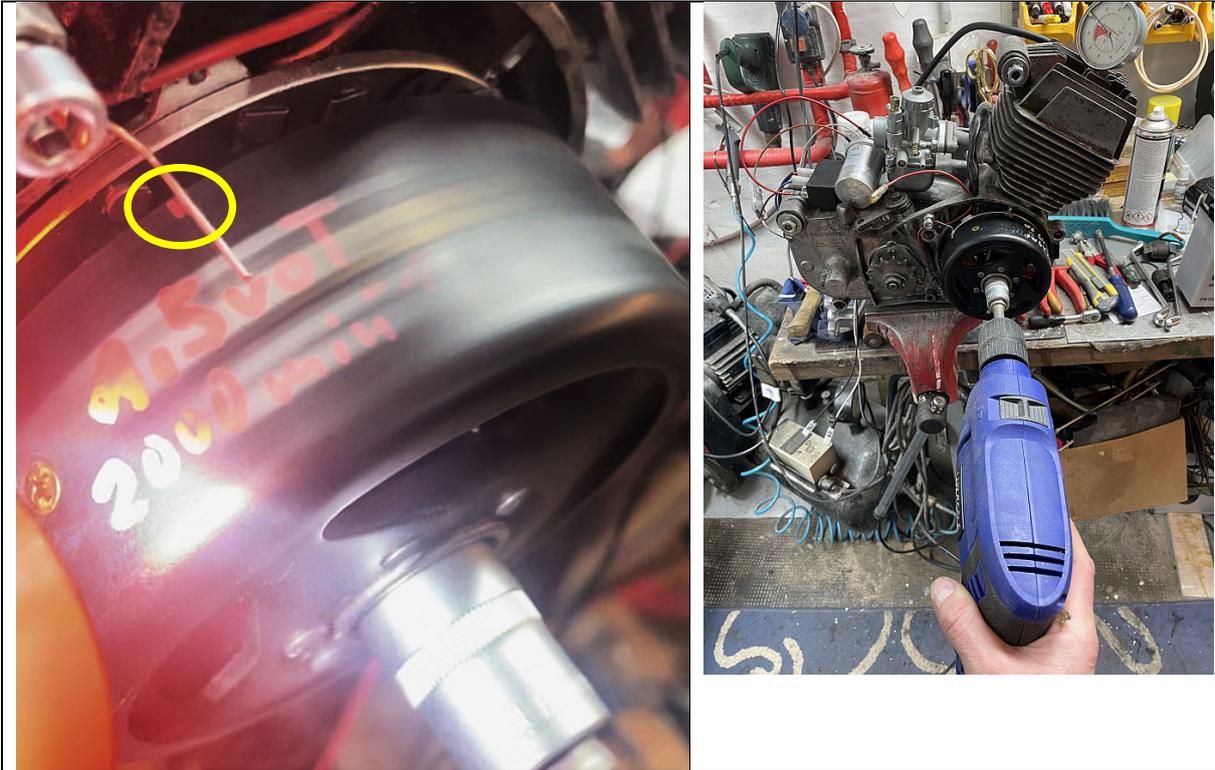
Zu früher Zündzeitpunkt sichtbar gemacht mit Stroboskop beim Rotieren des Motors mit der Bohrmaschine und ohne Zündkerze oder Messuhr.
